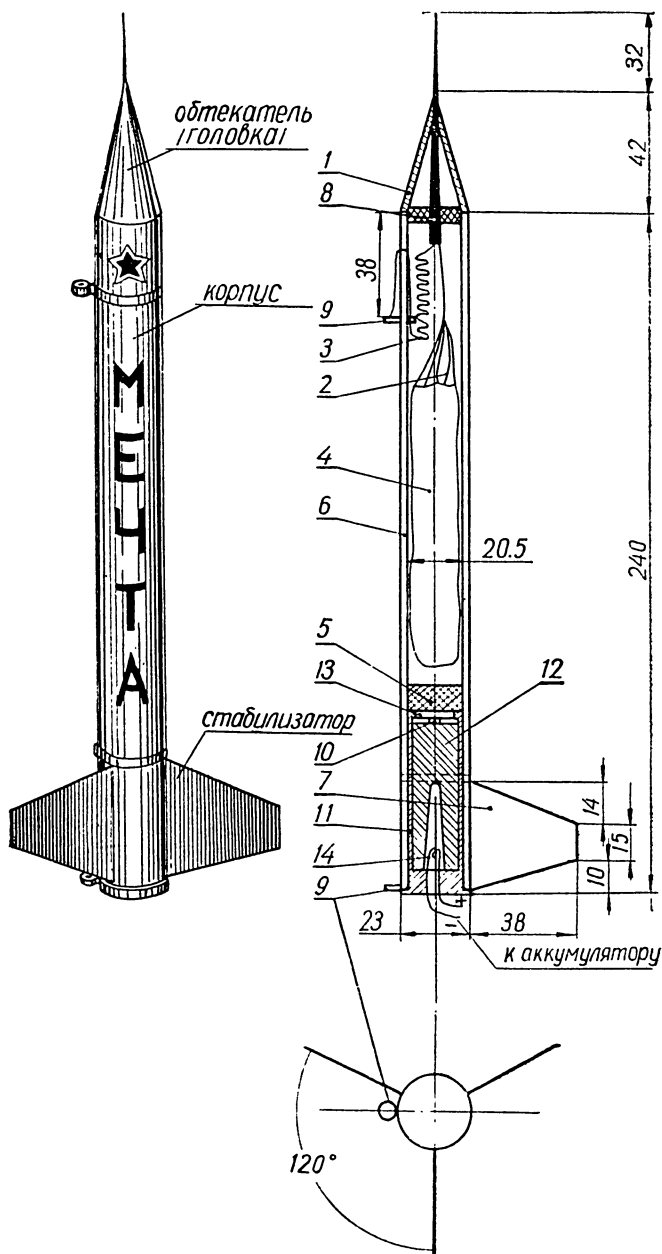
Общий вид и чертеж модели одноступенчатой ракеты «Мечта»: 1 — головка (обтекатель); 2 — стропы парашюта; 3 — амортизатор (резина); 4 — парашют; 5 — пыж из войлока или пенопласта; 6 — корпус; 7 — стабилизаторы; 8 — стержень; 9 — стартовые кольца; 10 — пыж картонный с отверстием; 11 — ракетный патрон; 12 — ракетный заряд; 13 — вышибной заряд для парашюта; 14 — электрозапал.
